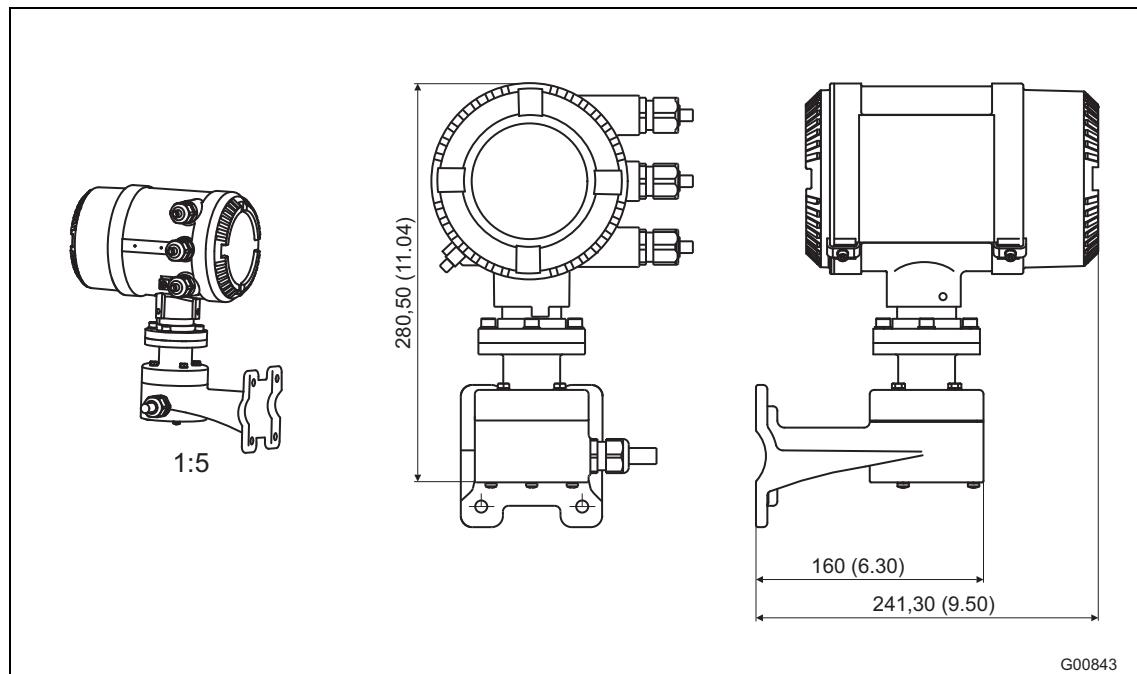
габариты корпуса измерительного преобразователя МЕ26 / 27 / 28
